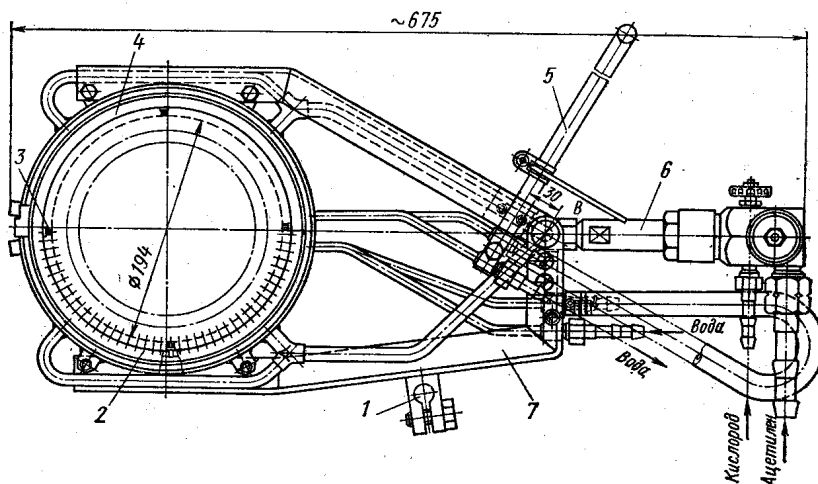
Кольцевая горелка серии КГ для газопрессовой сварки:
